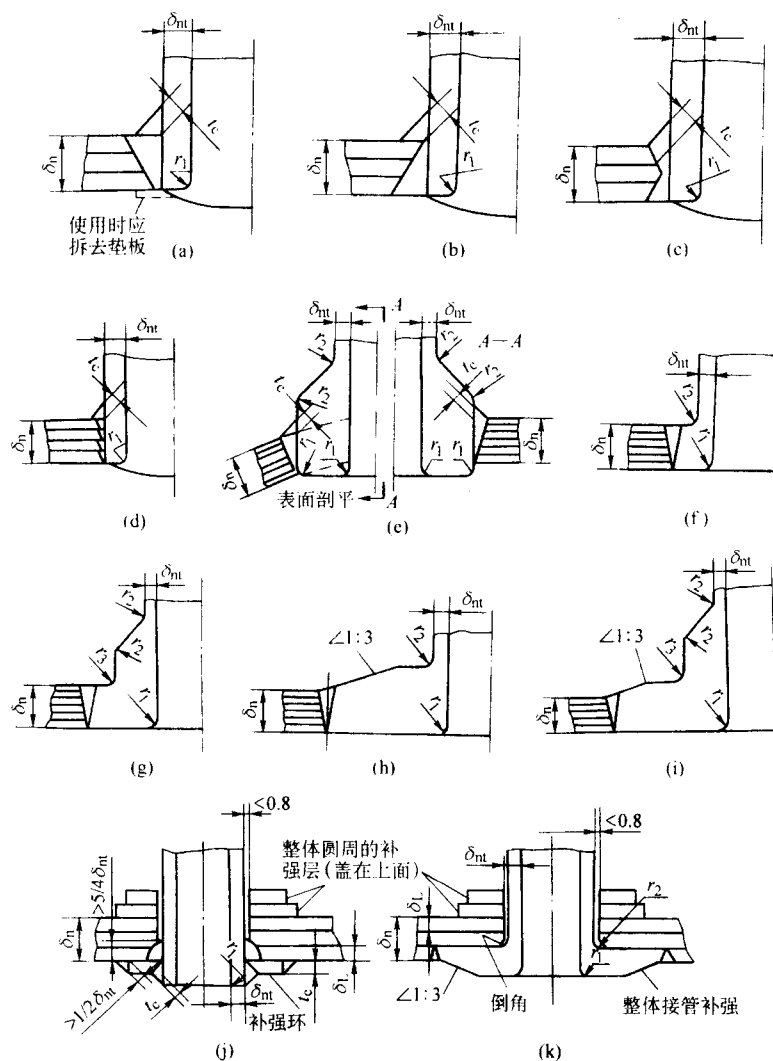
接管与多层容器壳体的焊接接头
